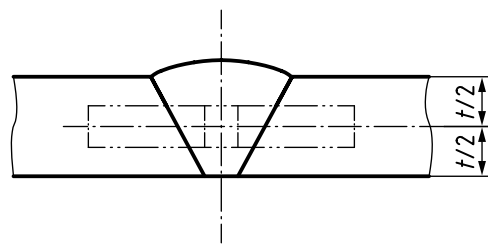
Position de l'éprouvette entaillée d'essai de flexion par choc dans la pièce d'essai
